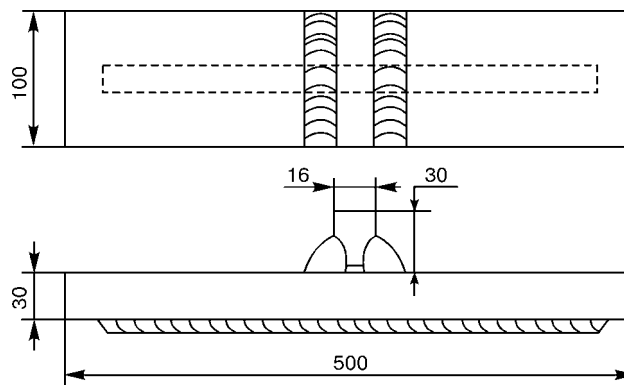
Сварной образец из высокопрочной стали для усталостных испытаний
